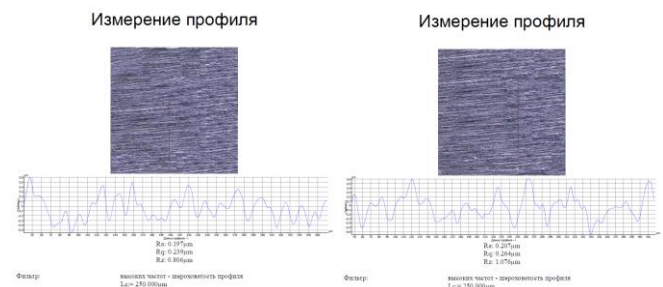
Шероховатость поверхности детали при зубохонинговании с помощью хона
